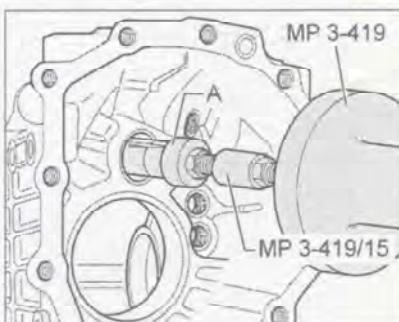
Извлечение внутренней обоймы игольчатого подшипника.
